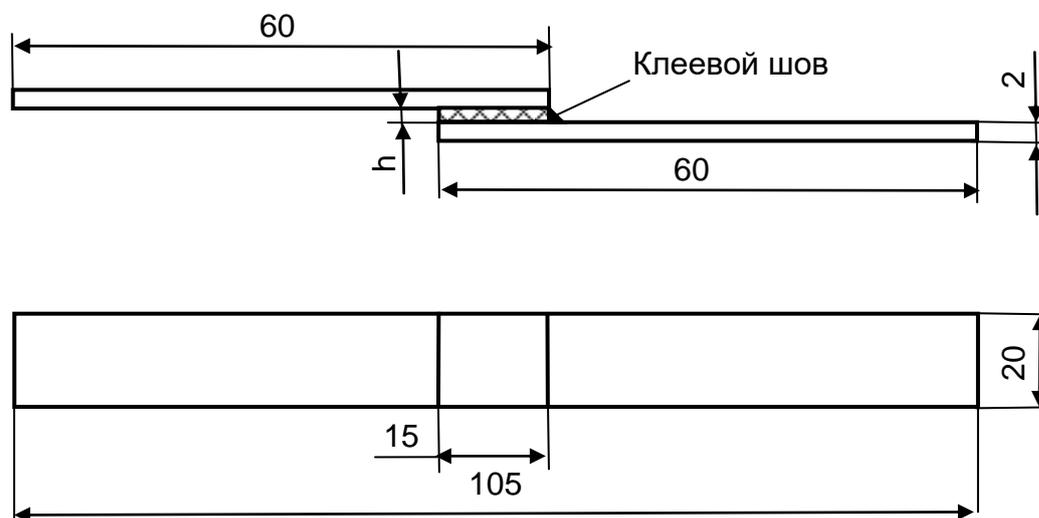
Форма и размеры образцов для испытаний клеевых соединений на сдвиг
